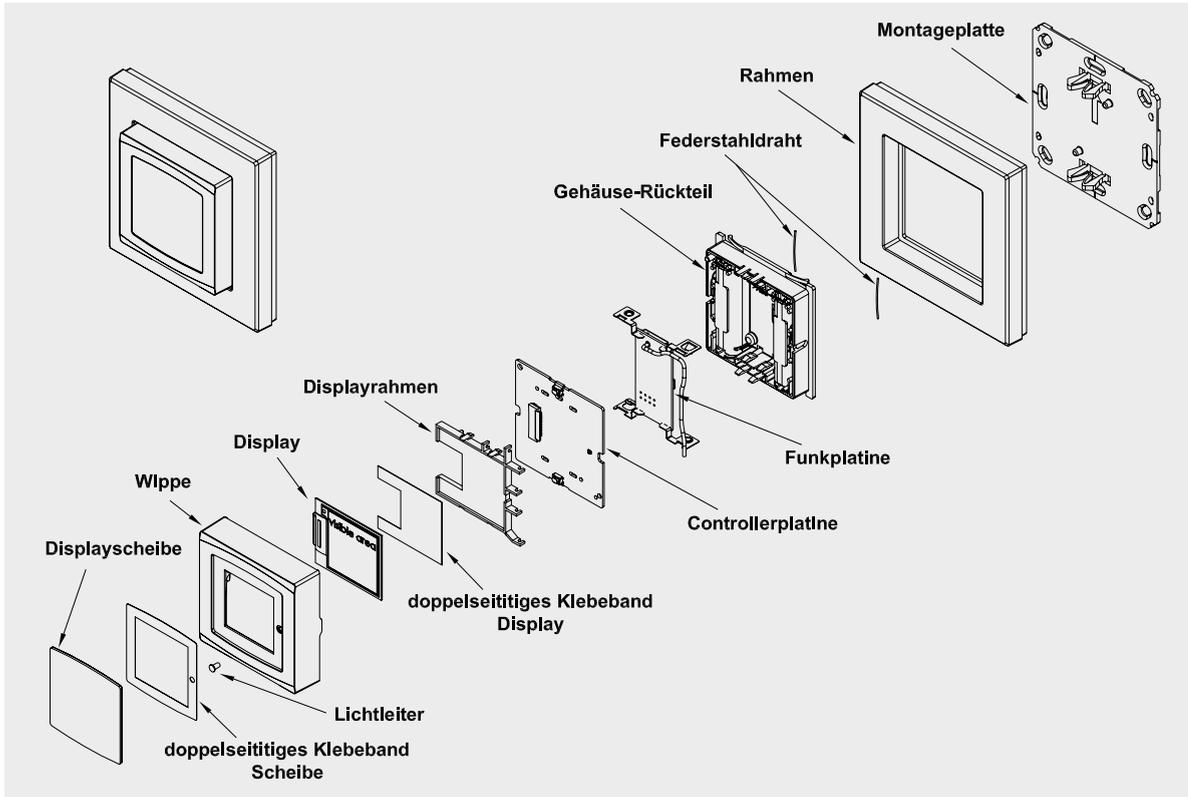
Die Explosionszeichnung gibt einen Überblick über den Gesamtaufbau des Geräts.
